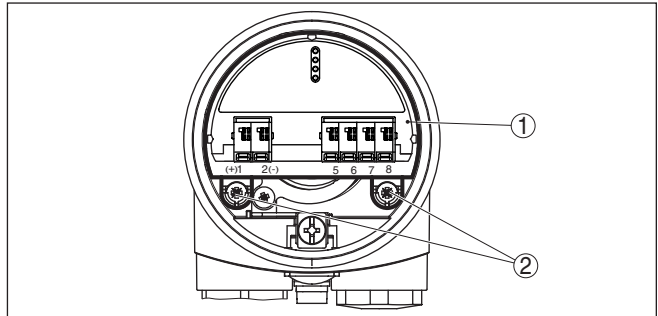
Soltar os parafusos de fixação do módulo eletrônico
